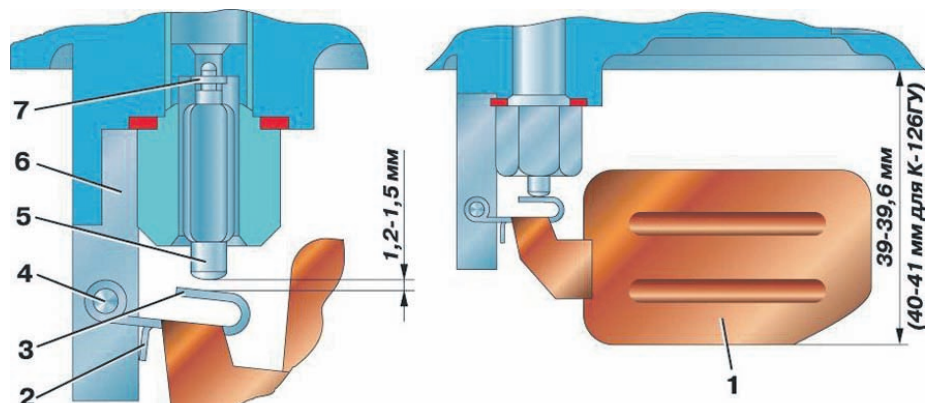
Поплавок карбюратора і його регулювання: 1 – поплавок; 2 – обмежувач ходу поплавка; 3 – язичок регулювання рівня; 4 – вісь поплавка; 5 – голка клапана; 6 – корпус клапана; 7 – шайба клапана
